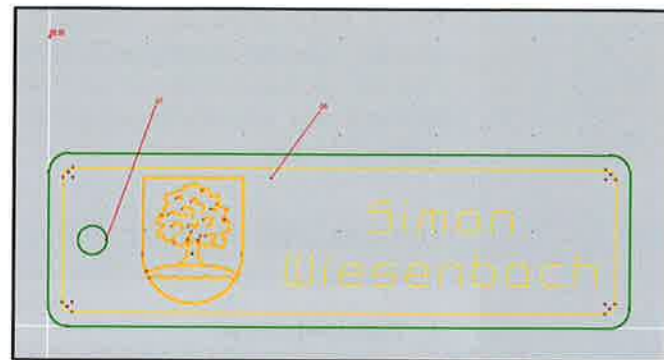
nccad-Zeichnung für einen Schlüsselanhänger
